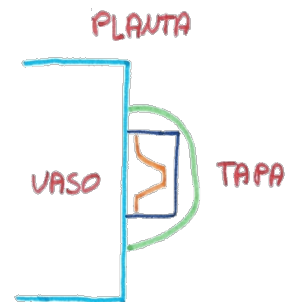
Columna media con un zigzag vertical (planta).
